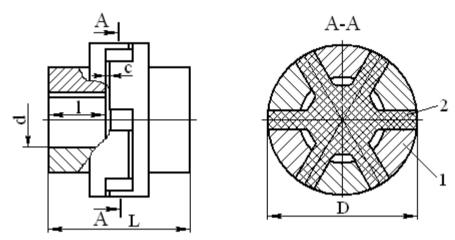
Муфта упругая с резиновой звездочкой: 1 - полумуфта; 2 - звездочка
